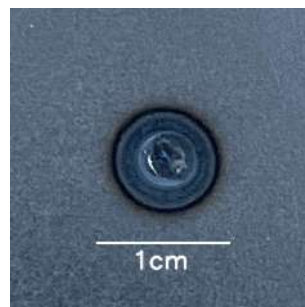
Ejemplo de imagen de superficie del proceso de soldadura por puntos estandarizada a 350×350 píxeles.
